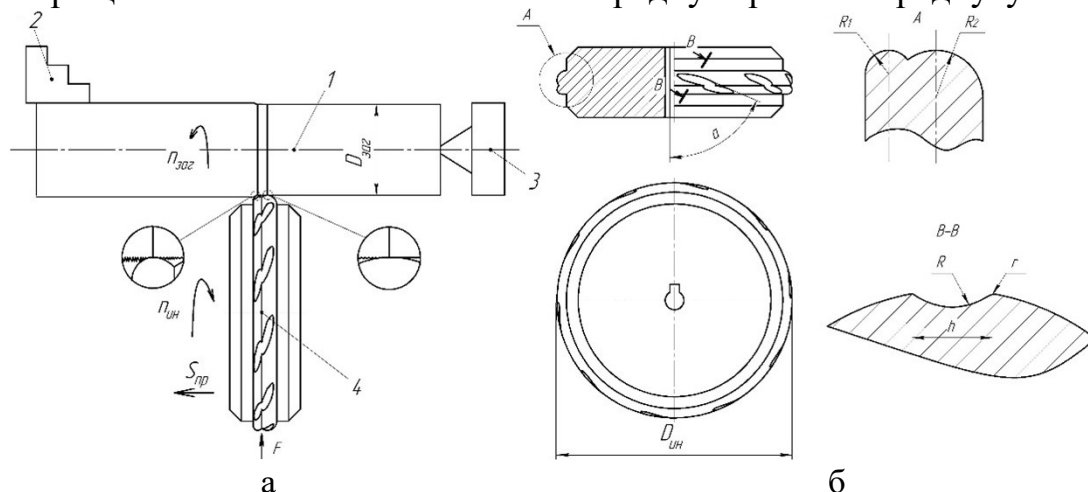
Схема ротационного поверхностного пластического деформирования (а) и геометрия сегментированного ролика (б): 1 – заготовка; 2 – трехкулачковый патрон; 3 – центр задней бабки; 4 – сегментированный ролик
